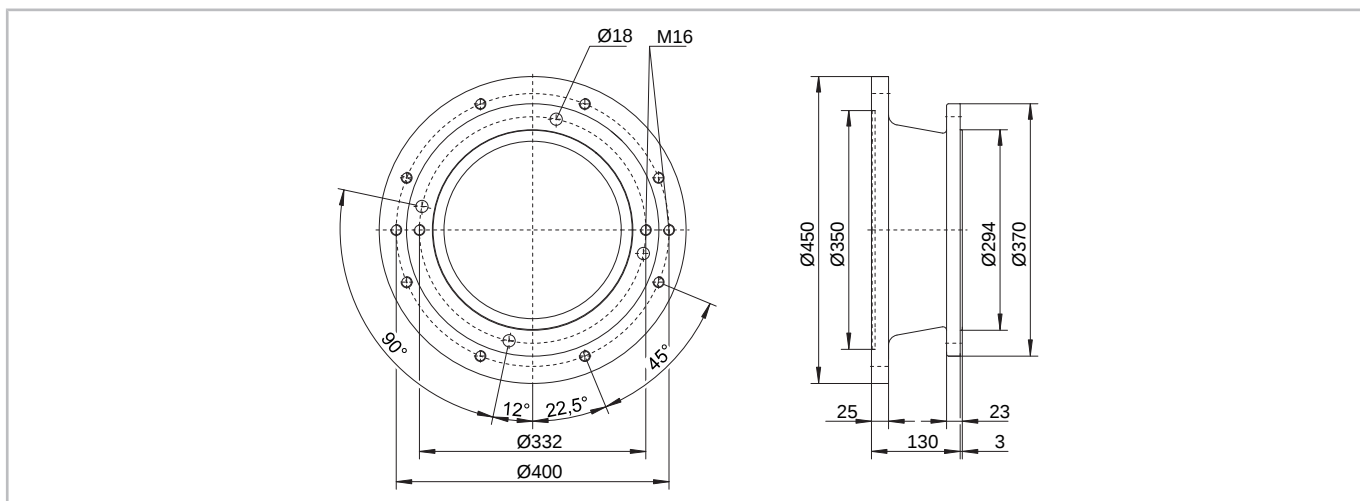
Габаритный чертеж кожуха муфты GS7100
